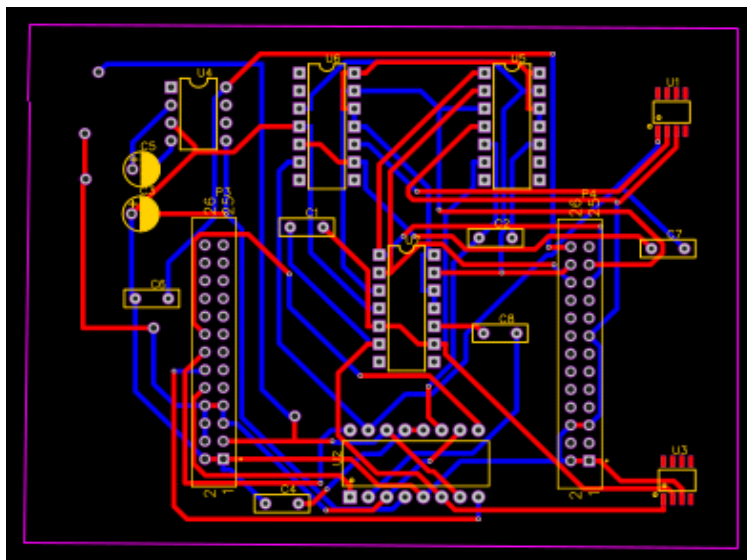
Schéma du PCB de la carte de TP 3 généré par EASYEDA
